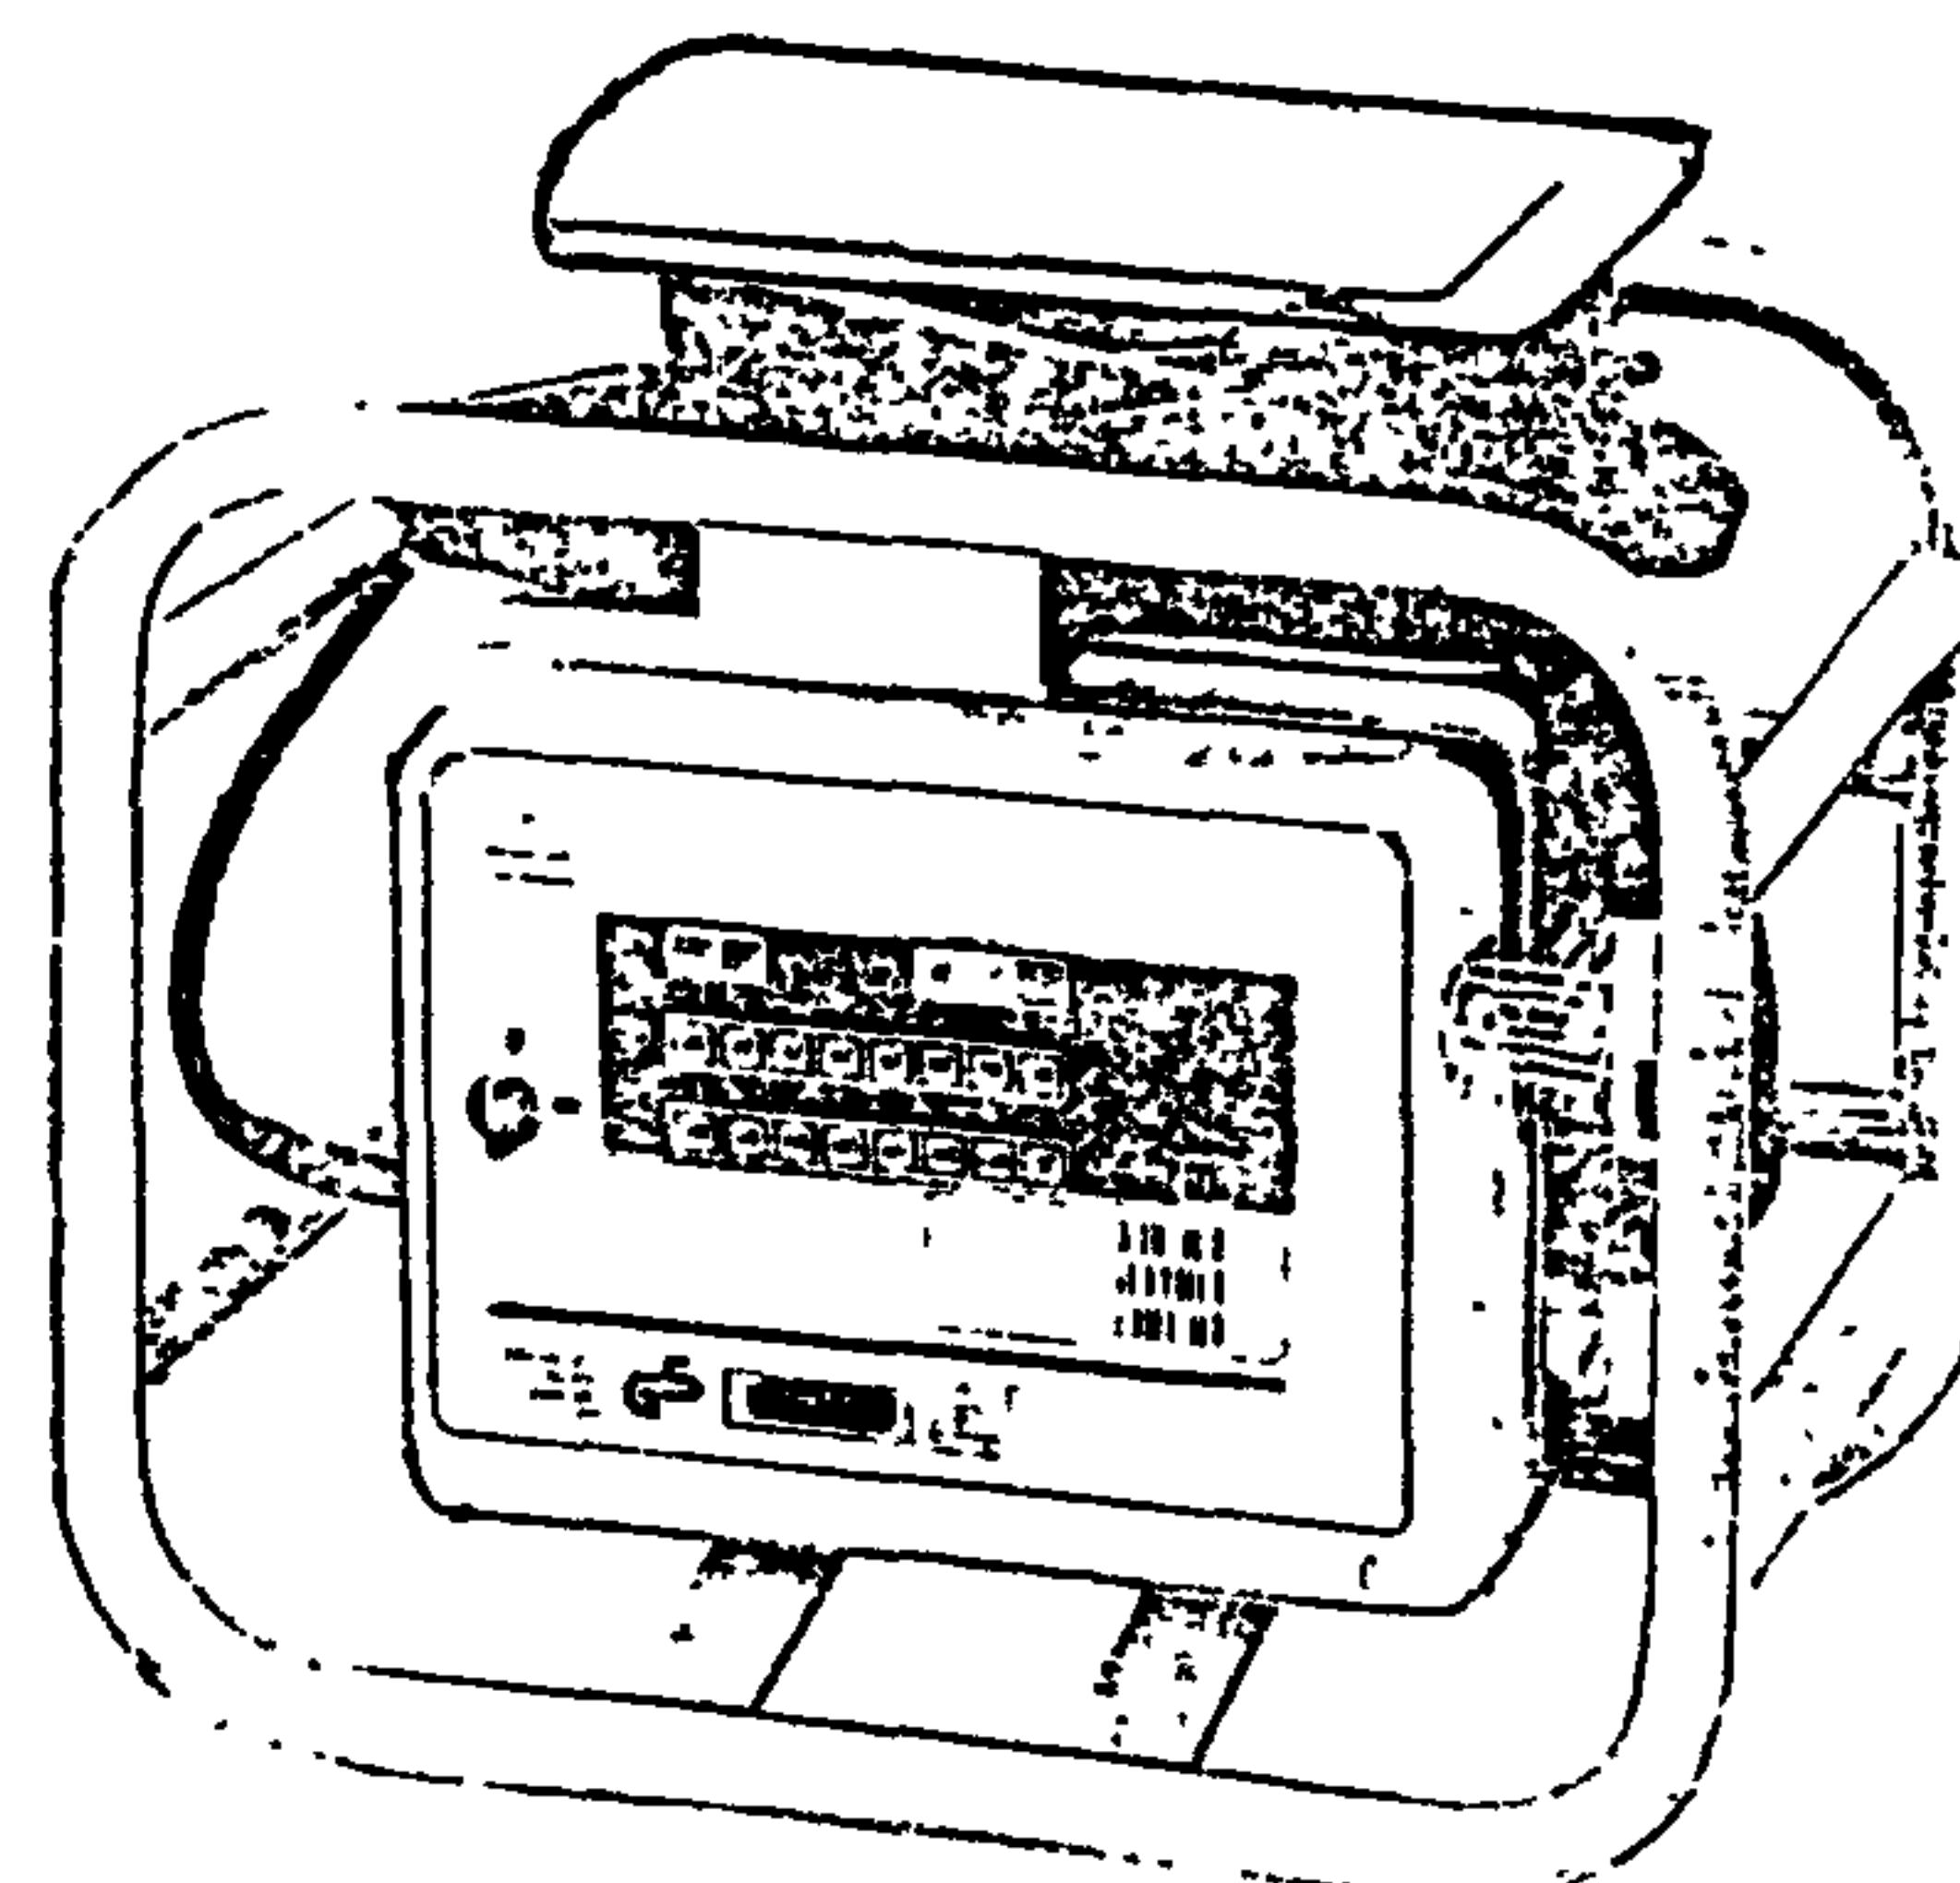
Пульт управления процессом сварки труб при помощи муфт с закладными нагревателями
